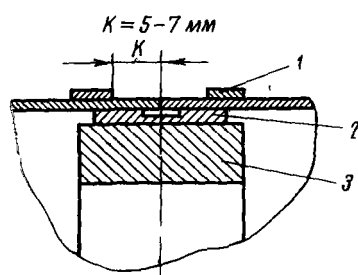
Сборка обечаек под сварку кольцевого шва:
